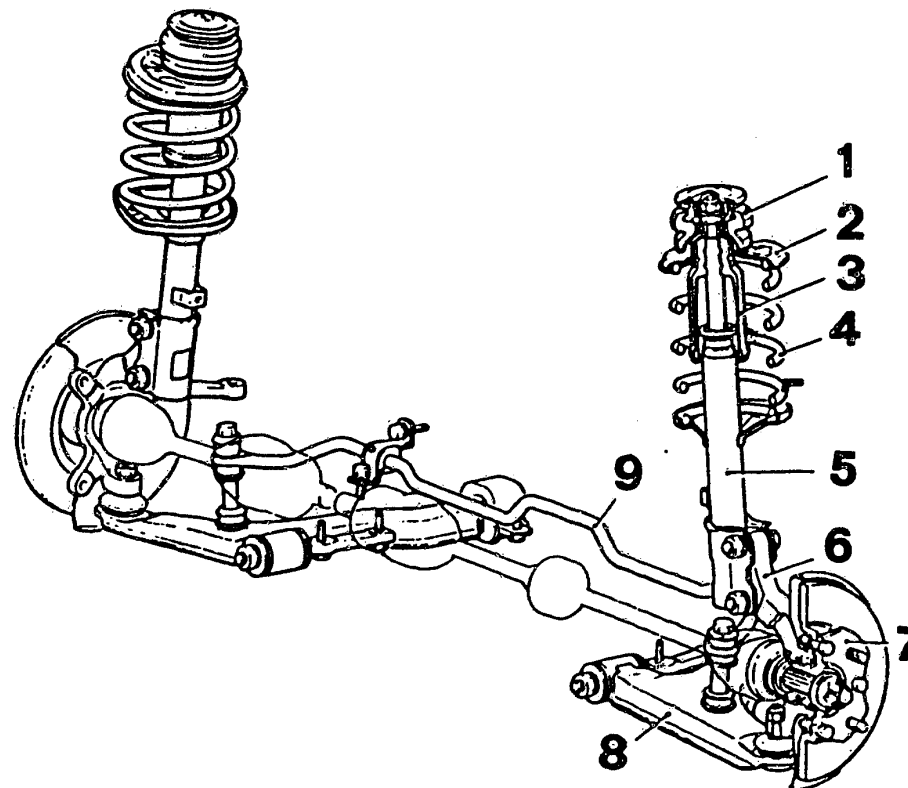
Vorderradaufhängung, teilweise geschlüsselt: 1 Gummidämpfer – 2 Federsitz – 3 Anschlaggummi – 4 Schraubenfeder – 5 Federbein – 6 Achsschenkel – 7 Radnabe – 8 Querlenker – 9 Stabilisator.
